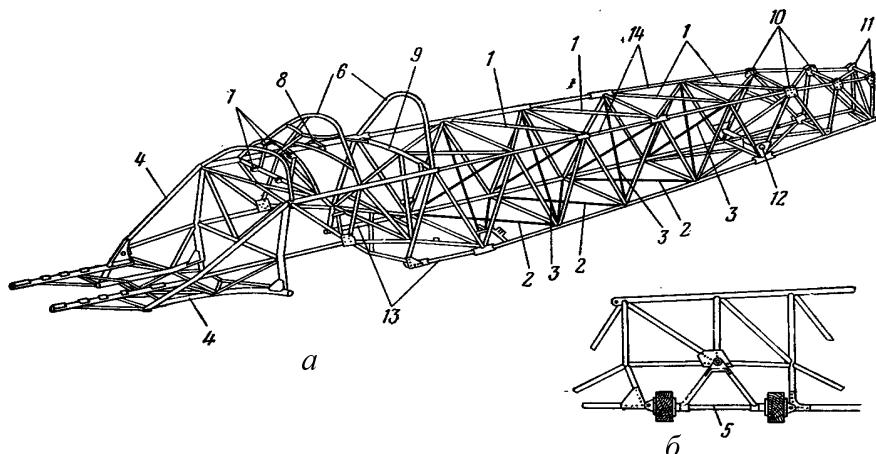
Фюзеляж ферменной конструкции (Як-1):
